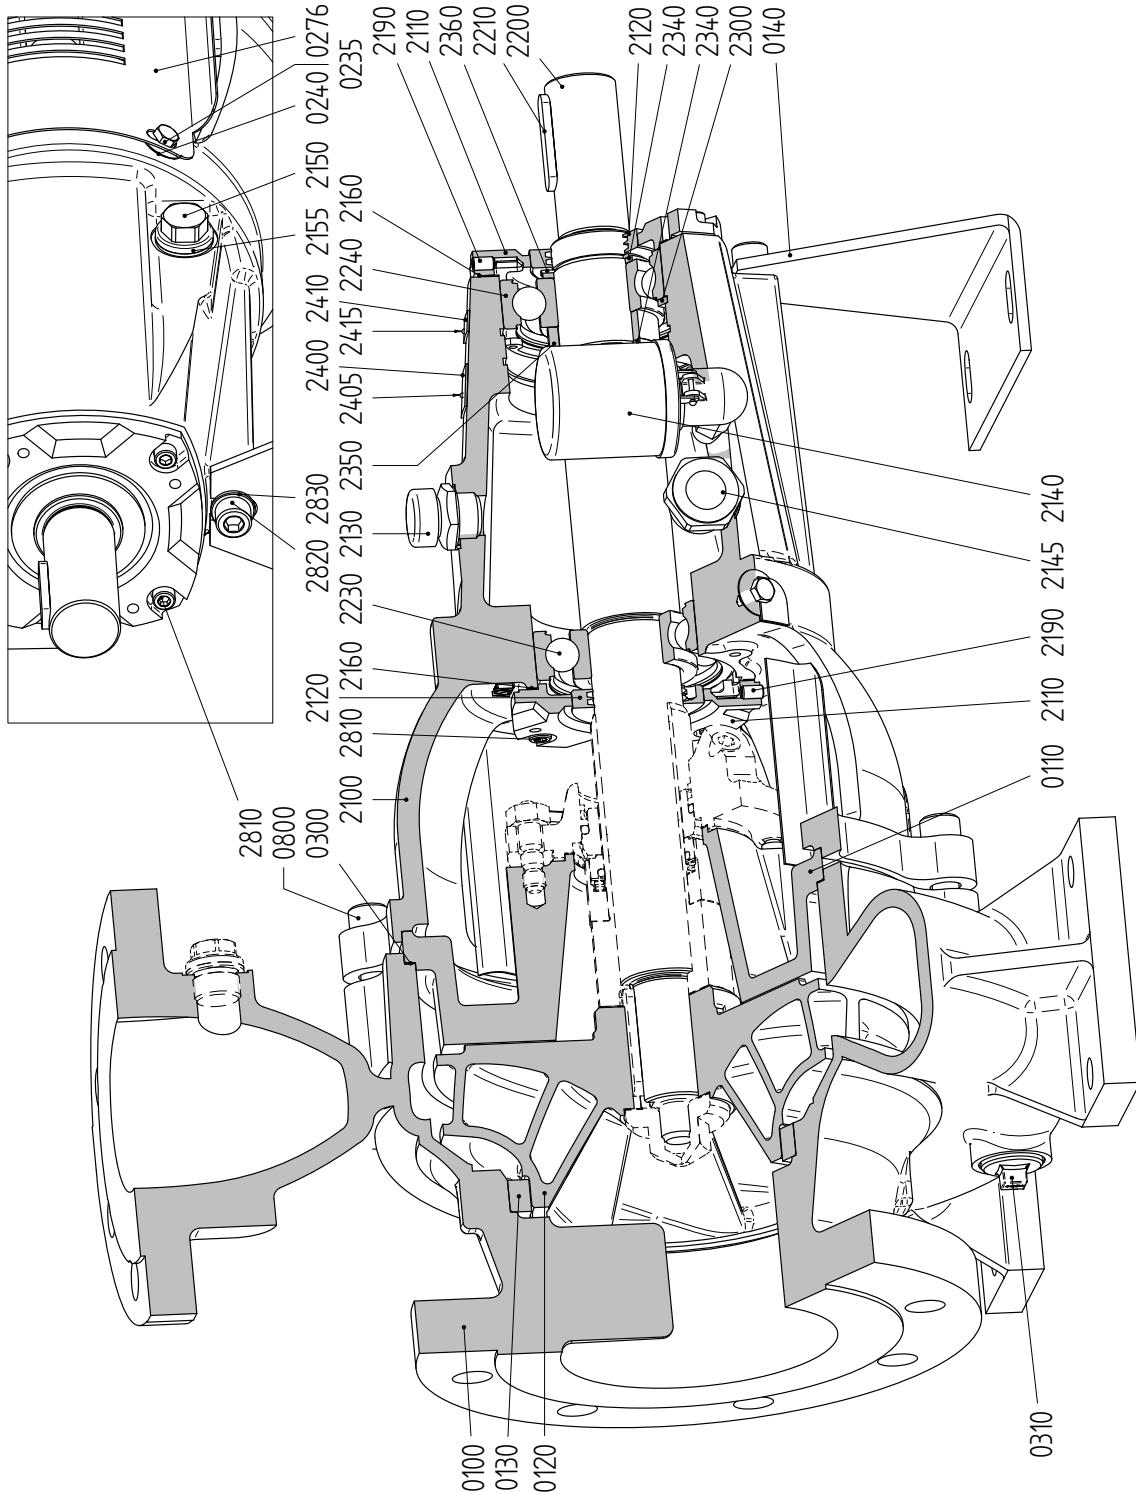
Чертеж в разрезе L3 с коническим отверстием — группы подшипников 1, 2, 3
